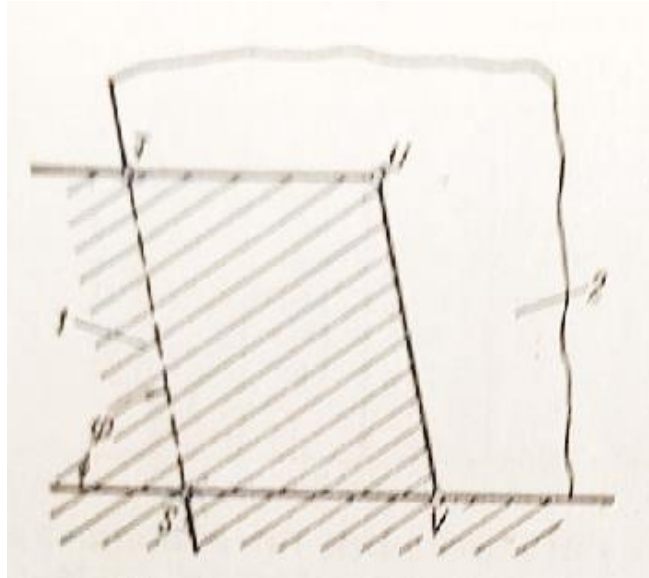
Точки первоначального контакта зуба торцевой фрезы с заготовкой: 1-Заготовка; 2- фреза
